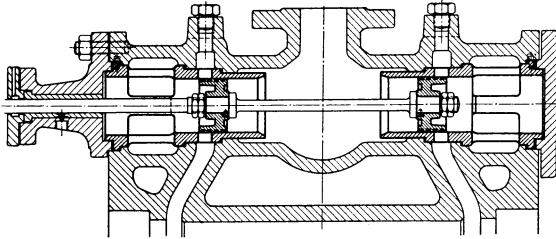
Ausführung: Dingersche Maschinenfabrik, Zweibrücken.
